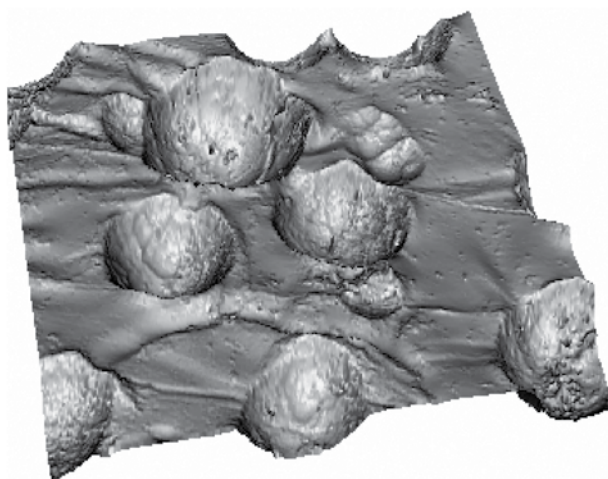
Топография поверхности листового металла после чистовой прокатки валками Torochrom
